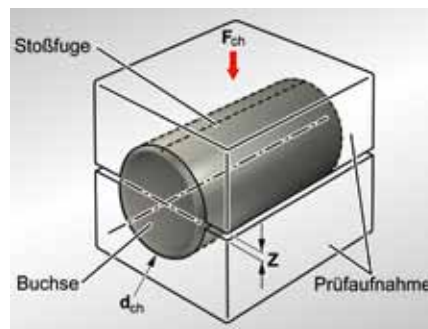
Prüfung Buchsenaußendurchmesser  $D_o$
